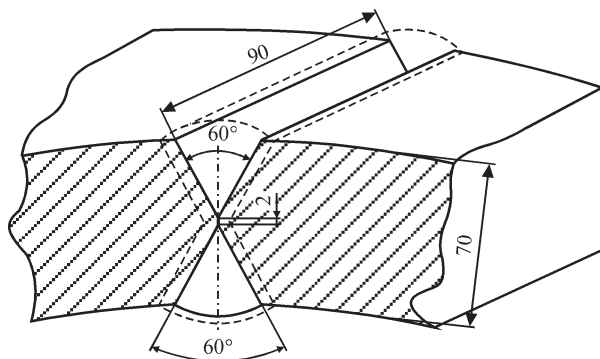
Подготовка стыка для двусторонней сварки колец
